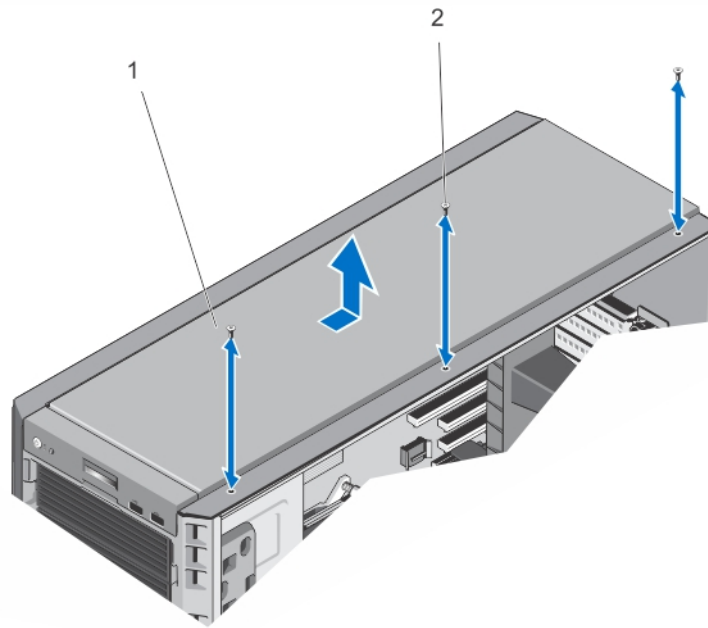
Extracción e instalación de la cubierta superior del sistema
